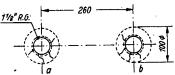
Im Kesselmantel eingeschraubte und verschweißte Gewindescheiben
